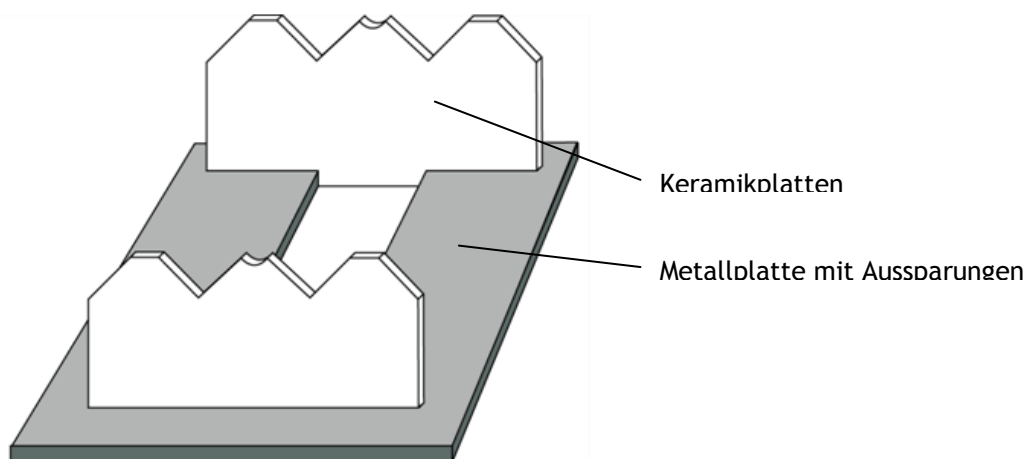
Halterung zum Schweißen der Winkelgeometrien
